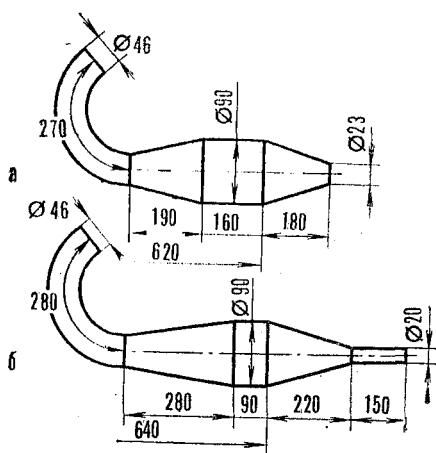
Система выпуска двигателя А. Савельева: а — для кросса; б — для шоссейно-кольцевых и ипподромных гонок
